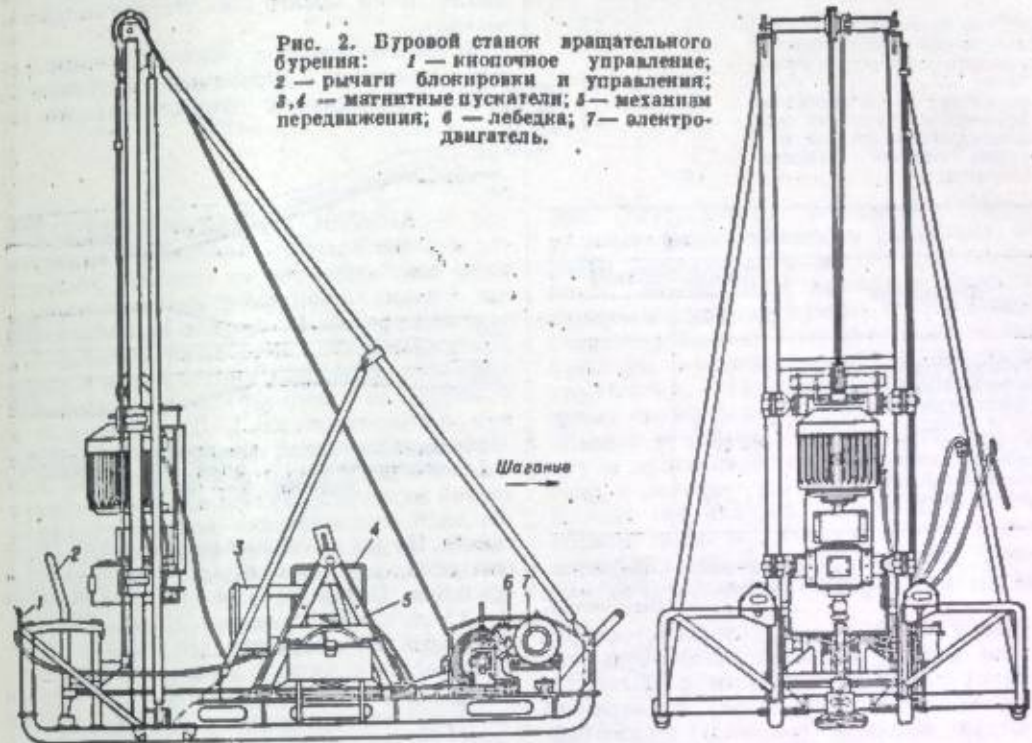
Буровой станок вращательного бурения: 1 — кнопочное управление; 2 — рычаги блокировки и управления; 3, 4 — магнитные пускатели; 5 — механик передвижения; 6 — лебедка; 7 — электродвигатель.
